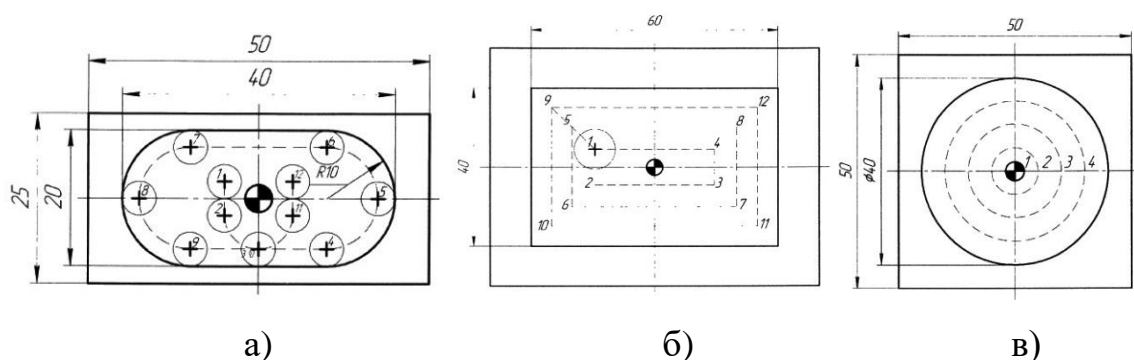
Чистова обробка кармана (а) та чорнова обробка прямокутного кармана (б), чорнове фрезерування круглого кармана
